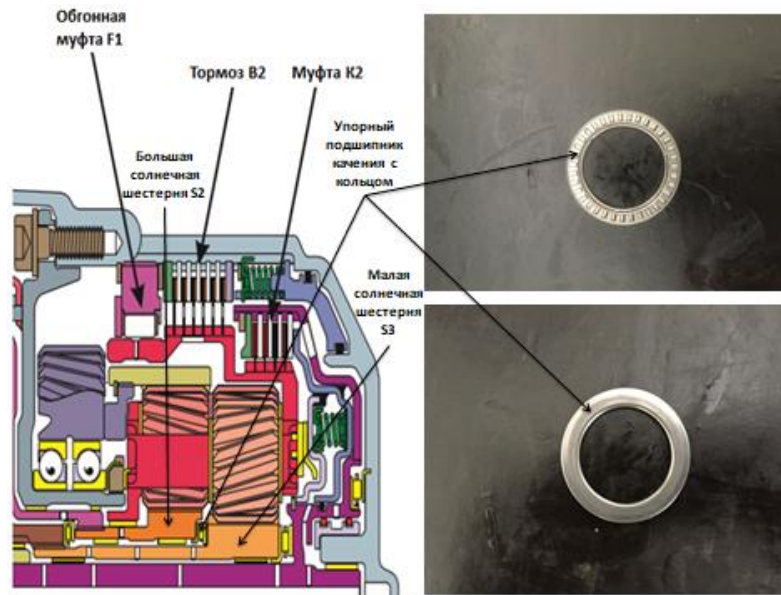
Назначение упорного подшипника качения с кольцом
